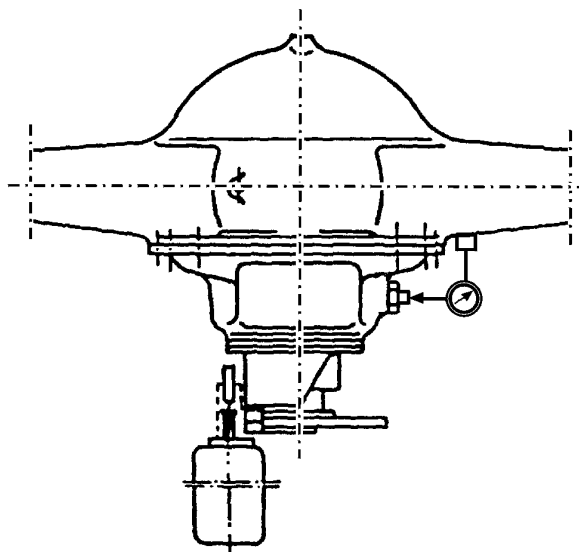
D.16. Проверка и регулировка осевого люфта (хода) ведущей шестерни главной передачи
